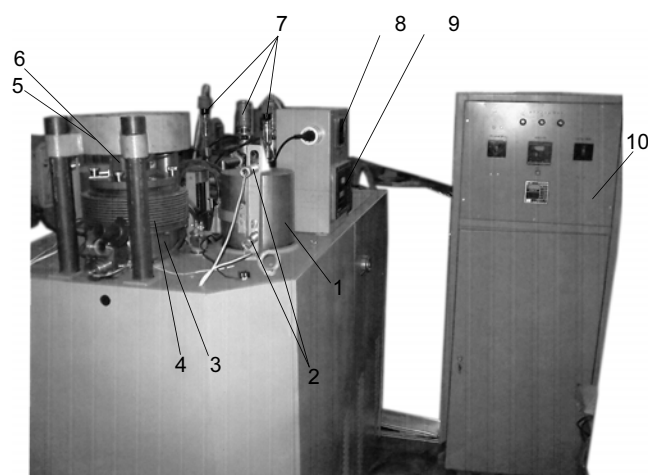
Установка УДС-1 для диффузионной сварки: 1 — камера загрузки; 2 — датчики положения камеры загрузки; 3 — камера сварки; 4 — сильфонный узел; 5 — силовой упор; 6 — силовое измерительное устройство; 7 — элементы вакуумной системы; 8 — датчик температуры; 9 — терминал ТВ-003/05Д; 10 — шкаф управления
